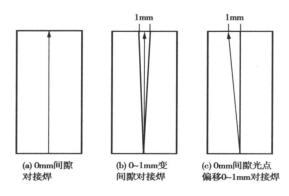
对接焊方式 Fig 1 Style of butt joint
